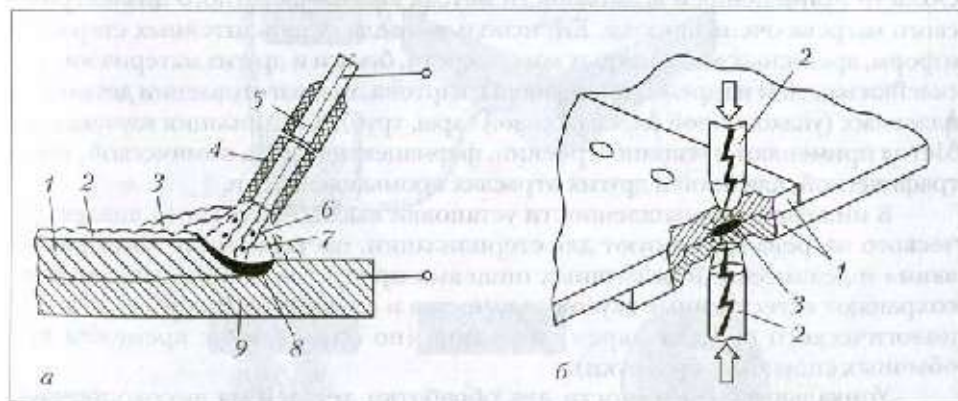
Виды электросварки: а — сварка плавящим (металлическим) электродом: 1 — сварной шов; 2 — шлаковая корка; 3 — защитная газовая атмосфера; 4 — электродное покрытие; 5 — электрод; б — электрическая дуга; 7 — капли электродного металла; 8 — сварочная ванна; 9 — заготовка; б — контактная точечная сварка: 1 — заготовки; 2 — электроды; 3 — сварная точка
